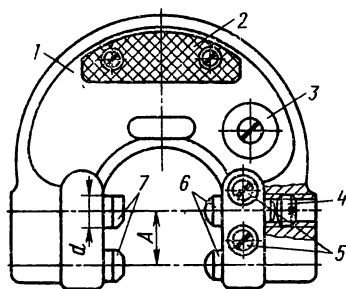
Скоба гладкая, регулируемая, с двумя подвижными вставками и двумя неподвижными пятками:
